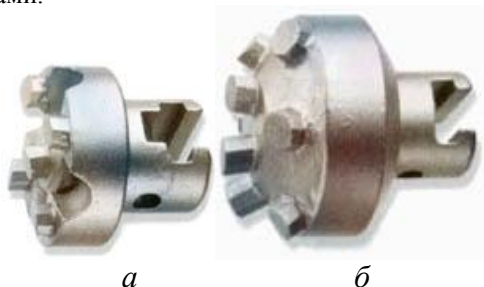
Буры с насадками из твердых сплавов: а – с регулируемыми режущими пластинками; б – с нерегулируемыми режущими пластинками.
